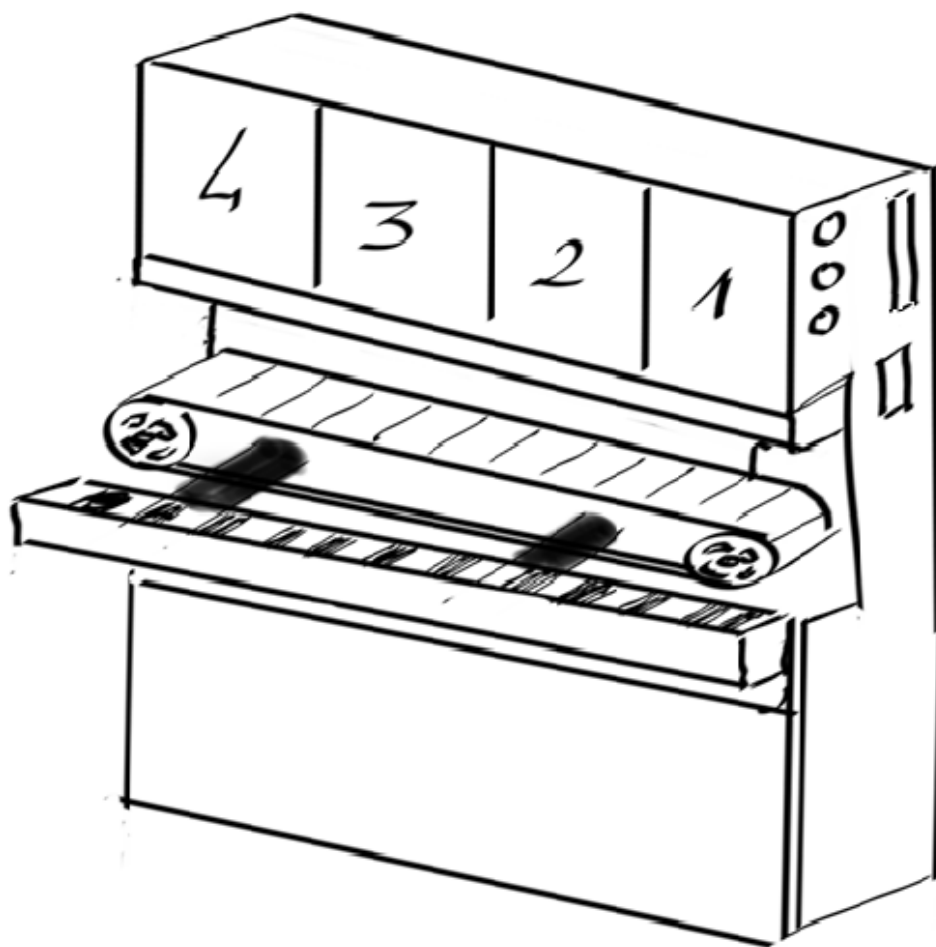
Máquina de disposición horizontal con una entrada frontal para el ingreso de los cortes de madera
